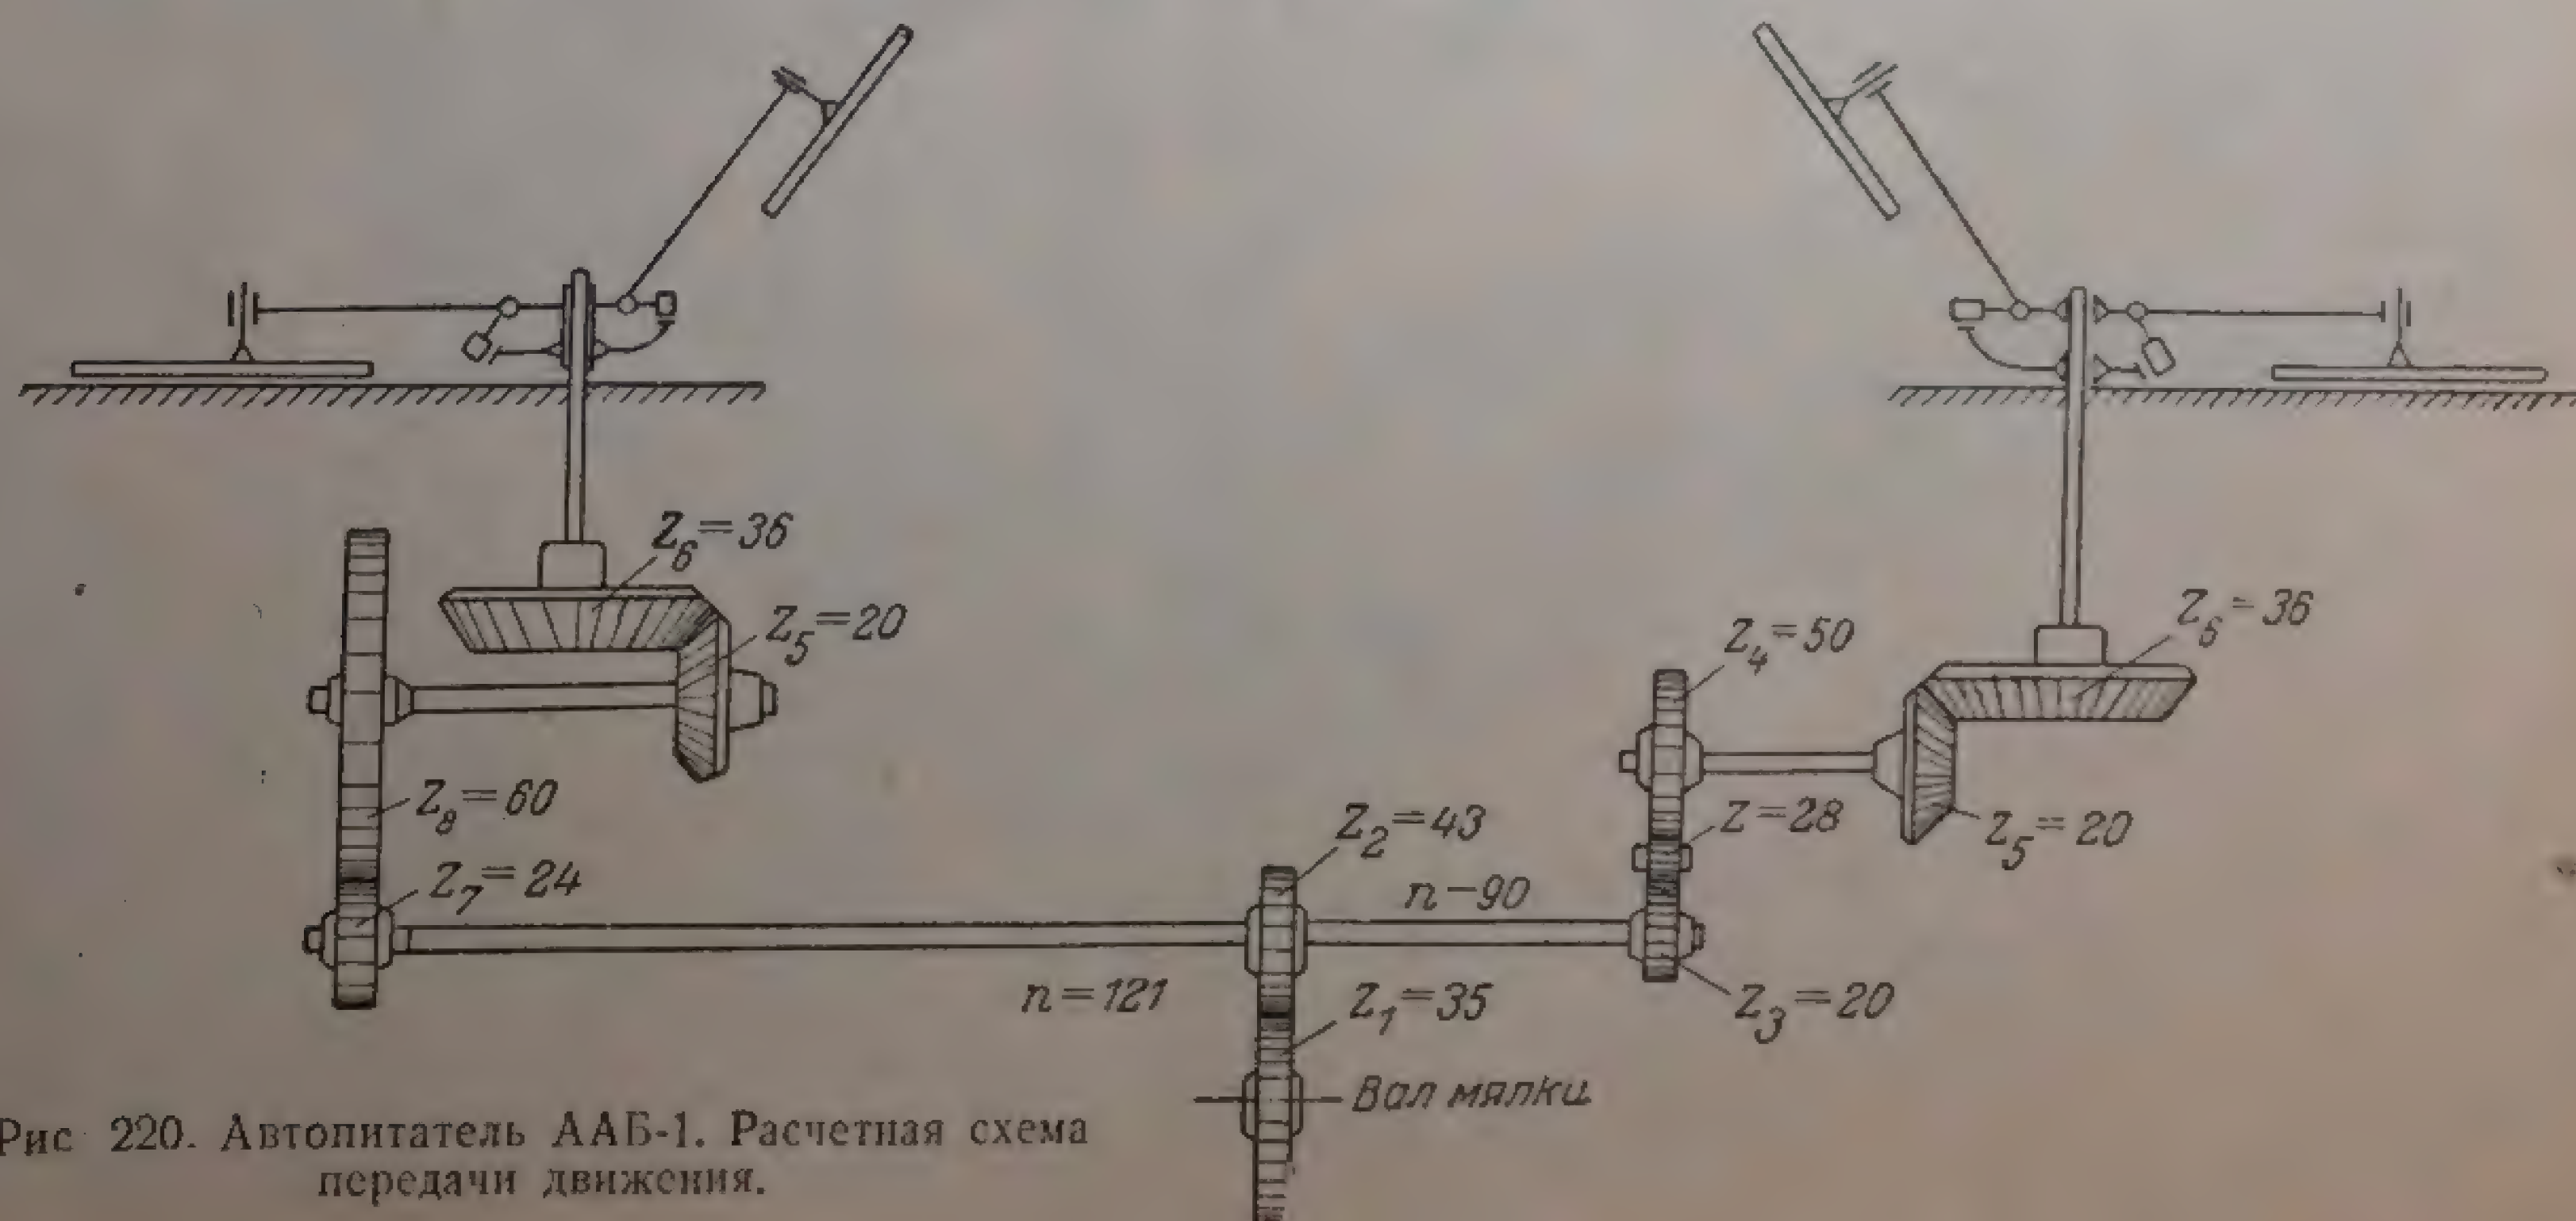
Автопитатель ААБ-1. Расчетная схема передачи движения.
